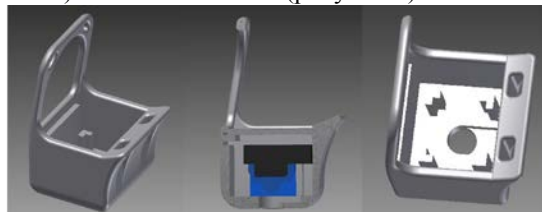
Сборка корпуса в САПР Autodesk Inventor
